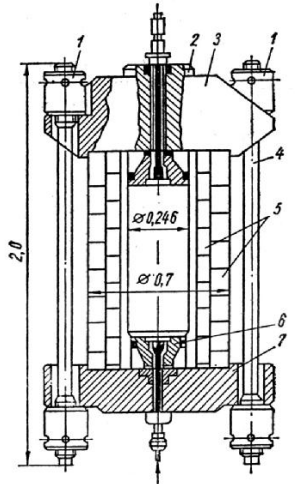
Устаткування для гідростатичного пресування (схема установки)
